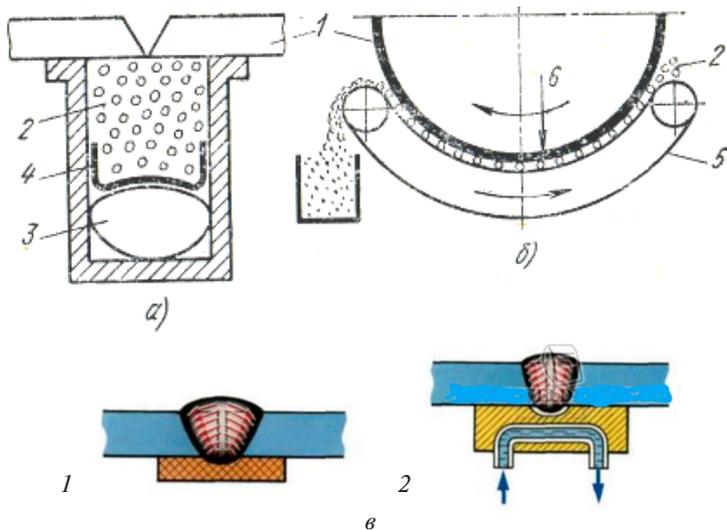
Схема устройства для формирования корня шва на флюсовой подушке: *а* – листы; *б* – трубы (1 – изделие, 2 – флюс сварочный, 3 – шланг, 4 – асбестовое полотно, 5 – лента транспортерная, 6 – положение сварочной горелки); *в* – подкладки (1 – графитовая, 2 – медная водоохлаждающая)
